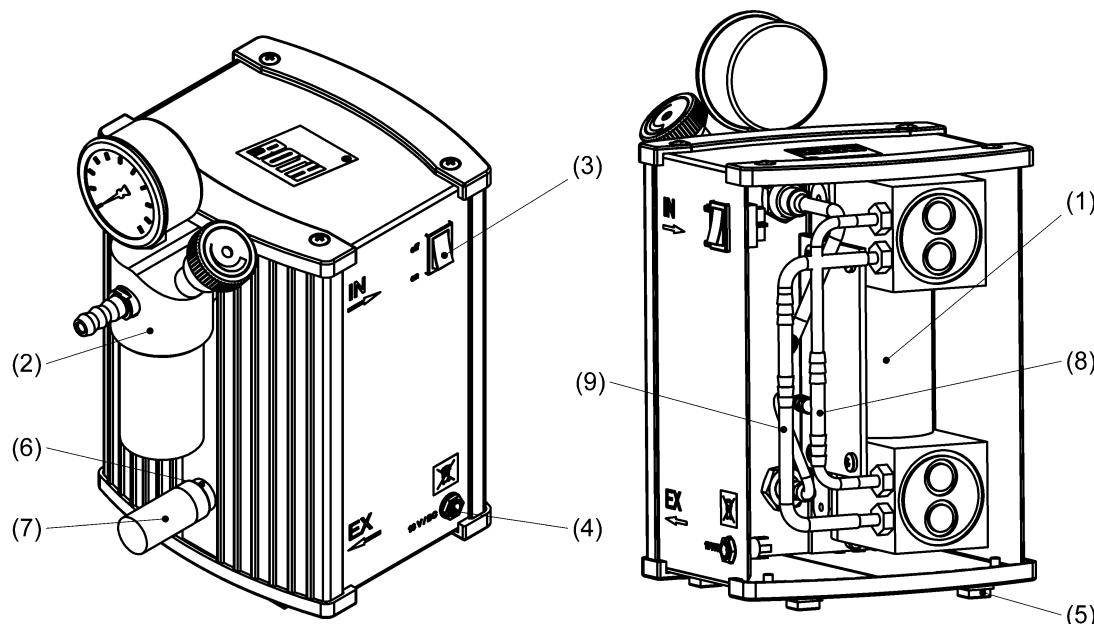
Pièces de rechange vue de devant et vue arrière (représenté sans paroi arrière)
